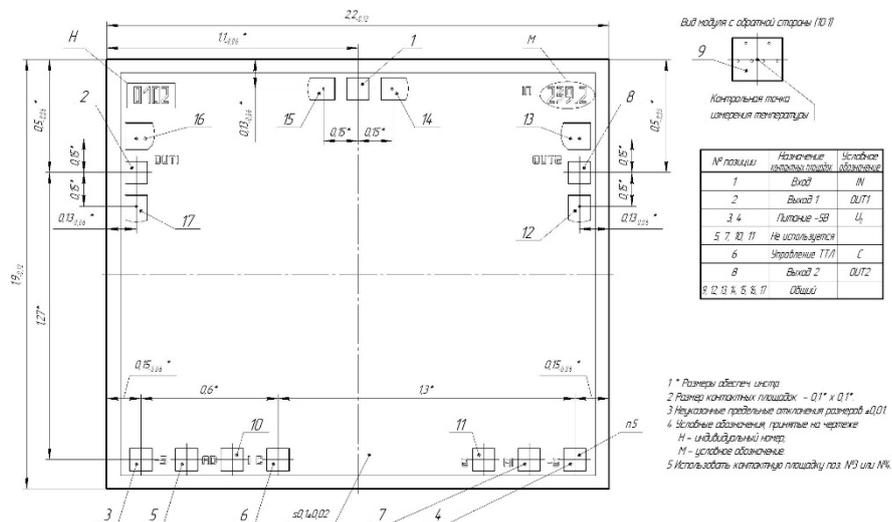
Внешний вид модуля М44228 (приемка "5"), габаритный чертеж.
